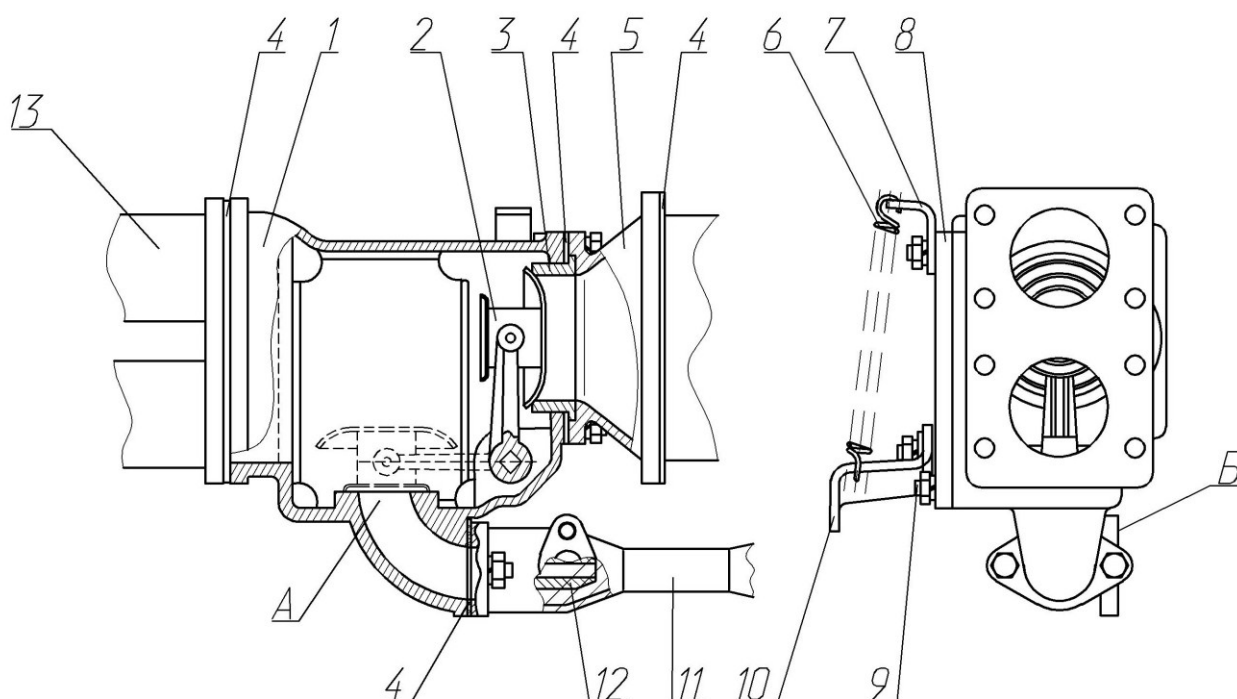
Газоструйный вакуум-аппарат АЦ-40(130)63Б: 1 – корпус; 2 – заслонка; 3 – седло; 4 – прокладка; 5 – конусный раструб; 6 – пружина; 7 – кронштейн; 8 – крышка; 9 – шпилька; 10 – рычаг; 11 – диффузор; 12 – сопло; 13 – трубопроводы выхлопного тракта двигателя; А – отверстие на газоструйный вакуумный насос; Б - фланец крепления трубопровода вакуумной системы.
